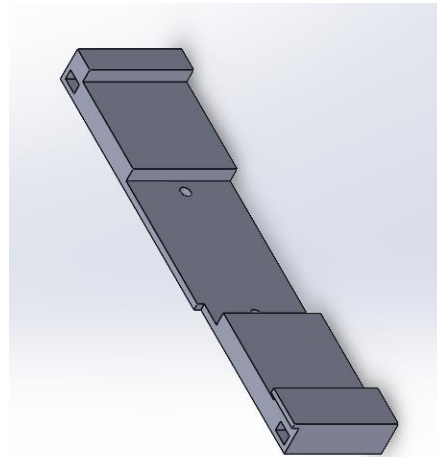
Diseño soporte sensor DLS 2. Fuente autor.
